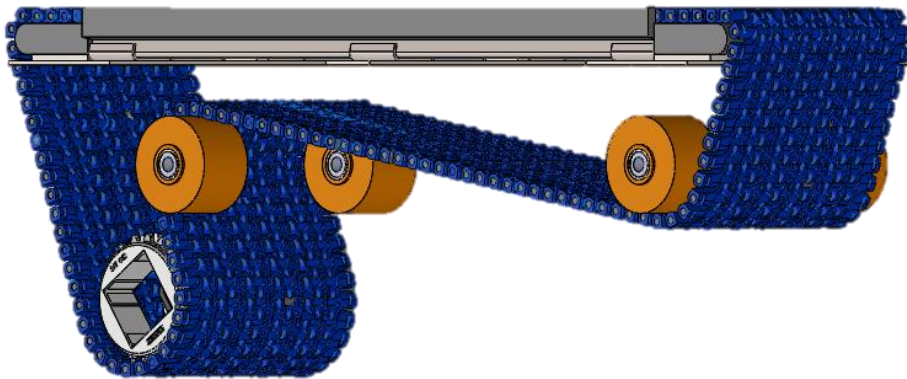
Dibujo CAD que muestra la posición de los Rodillos de apoyo en la directriz de diseño.
